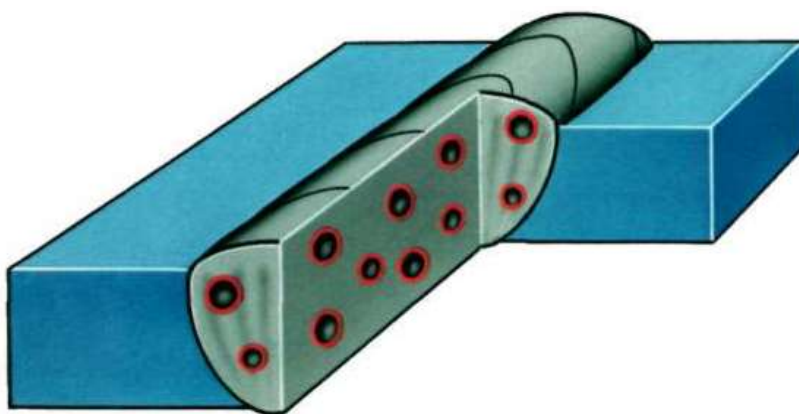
Дефекты сварного шва по типу равномерно распределенных пористостей
